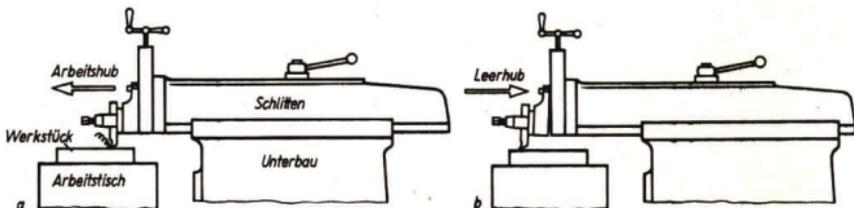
/1. Wirkungsweise der Kurzhobelmaschine
